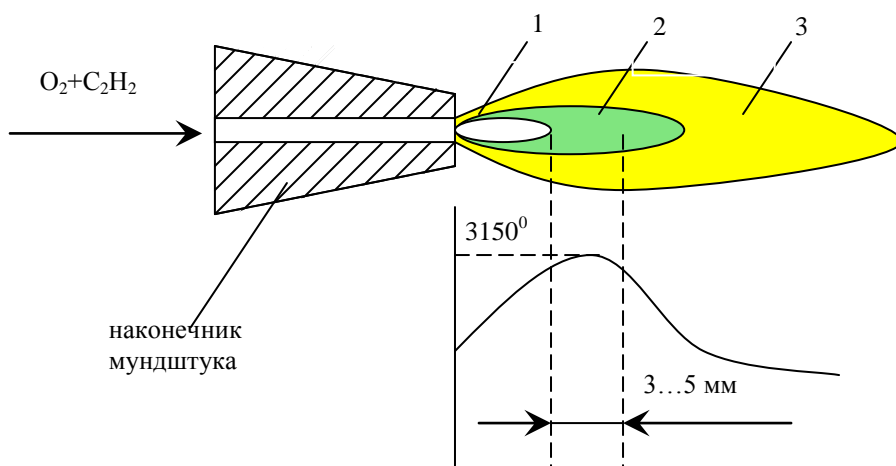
Схема сварочного пламени: 1-ядро, 2-восстановительная (рабочая) зона, 3-окислительная зона
